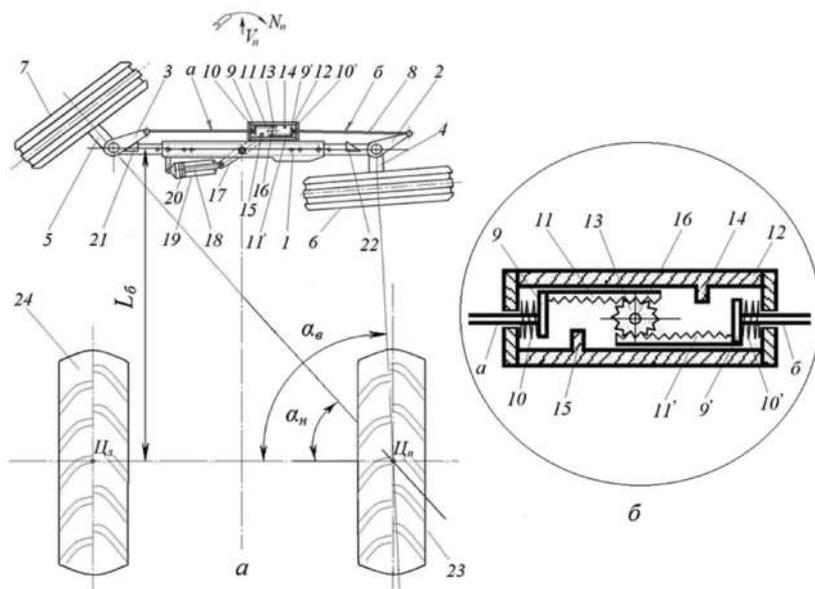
Четырехколесный трактор, снабженный новой конструкцией рулевого привода.
